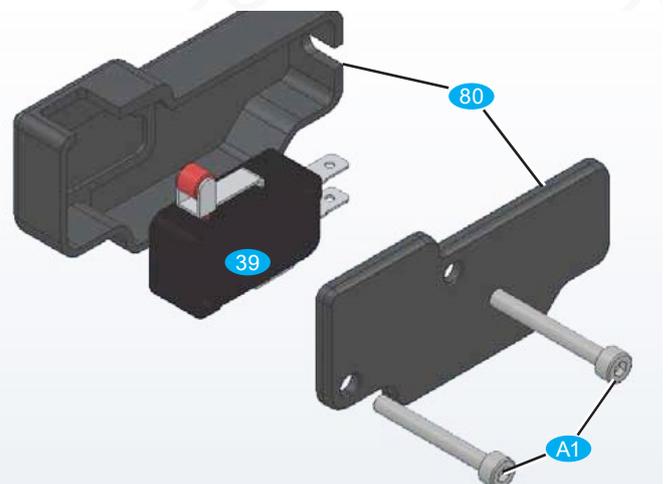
Baugruppe Referenzschalter / Gehäuse.
